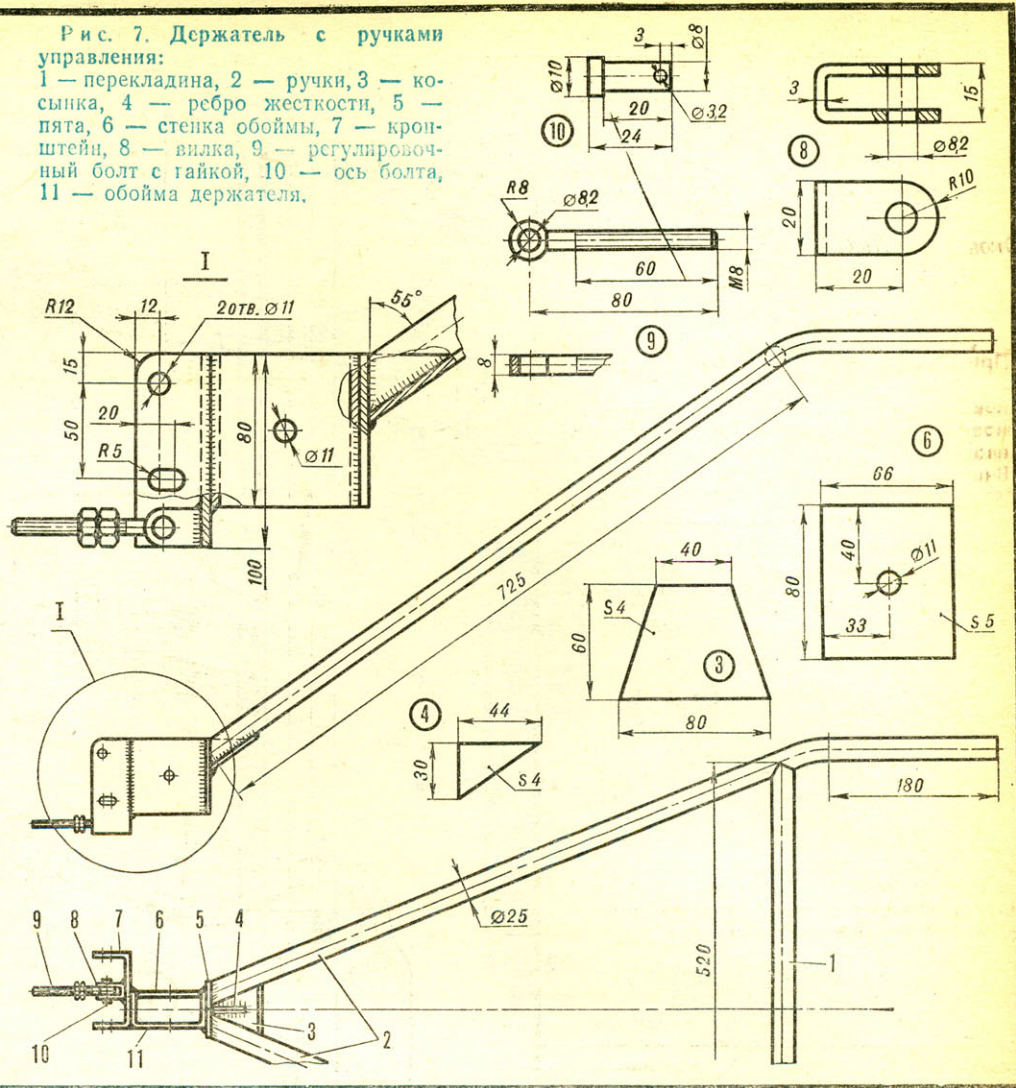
Держатель с ручками управления: 1 — перекладина, 2 — ручки, 3 — косынка, 4 — ребро жесткости, 5 — пята, 6 — стенка обоймы, 7 — кронштейн, 8 — вилка, 9 — регулировочный болт с гайкой, 10 — ось болта, 11 — обойма держателя.
